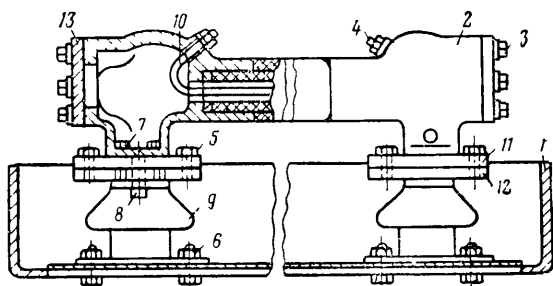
Главный высоковольтный предохранитель типа ЯП-22:
